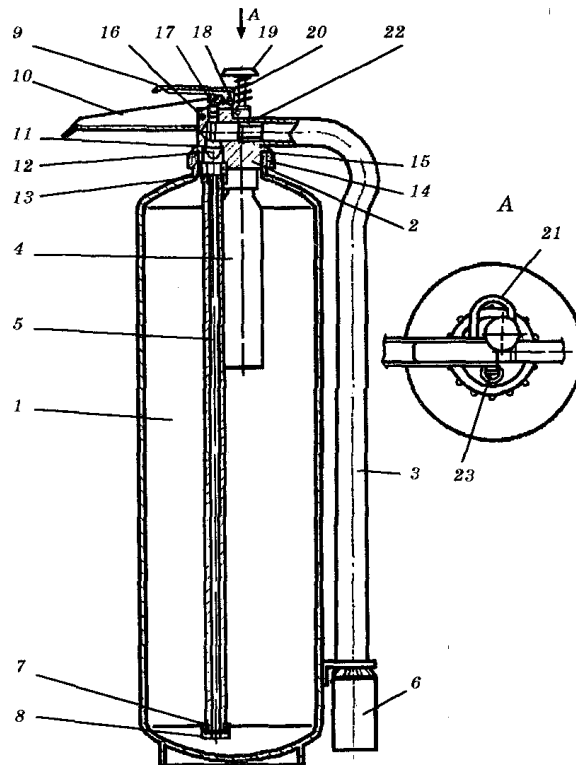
Вогнегасник повітряно-пінний ВПП-10: 1 – корпус; 2 – головка; 3 – рукав; 4 – балон з робочим газом; 5 – трубка сифонна; 6 – піногенератор; 7 – сітка; 8 – корпус фільтра; 9 – важіль керування клапаном; 10 – ручка; 11 – кільце ущільнювальне; 12 – клапан; 13 – перехідник; 14 – гайка накидна; 15 – кільце ущільнювальне; 16 – штифт; 17 – пружина; 18 – вісь; 19 – кнопка з голкою; 20 – пружина; 21 – запобіжна чека; 22 – кільце ущільнювальне; 23 – запобіжний клапан
